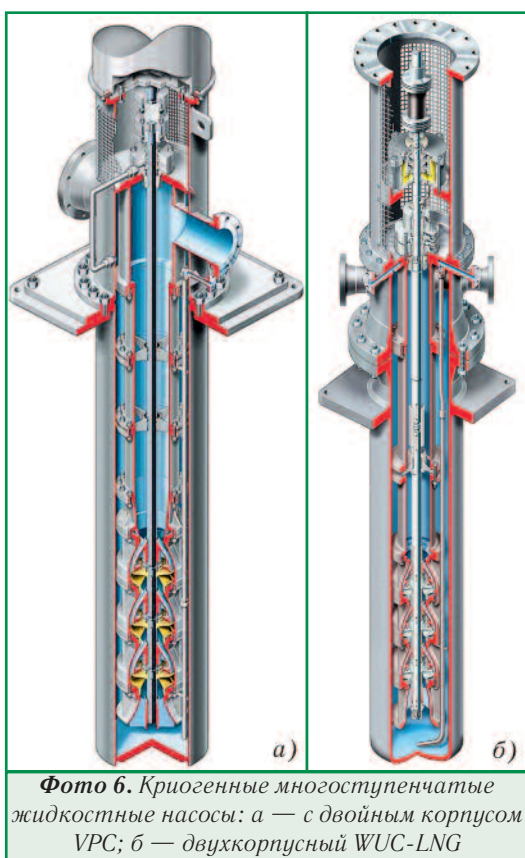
Криогенные многоступенчатые жидкостные насосы: а — с двойным корпусом VPC; б — двухкорпусный WUC-LNG
